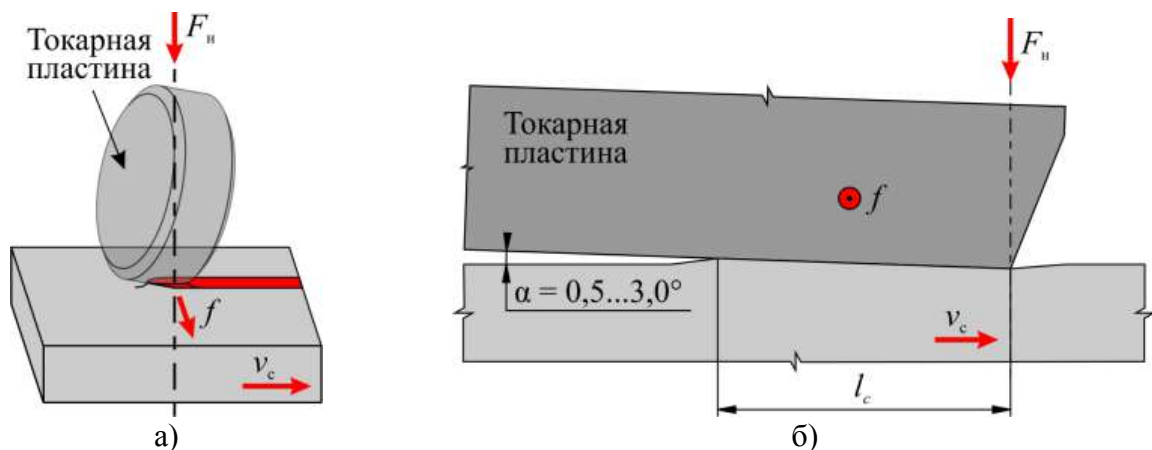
Схема клинового цилиндрического выглаживания плоской детали
